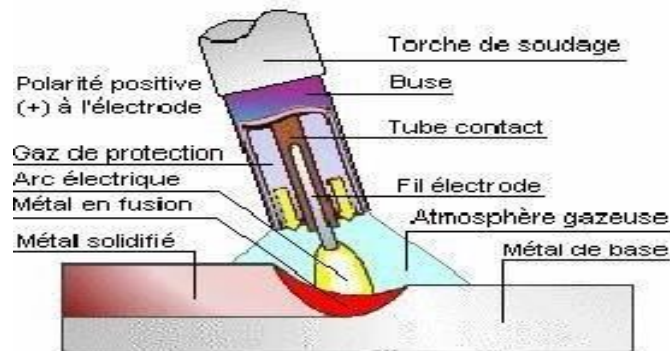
Procédés de soudage MIG/MAG
